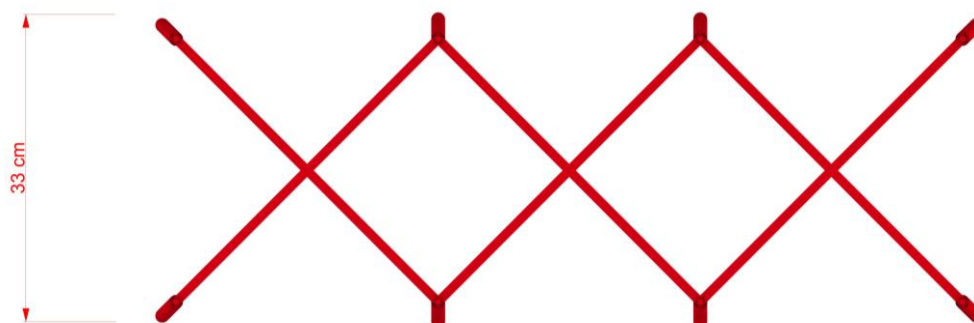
Původní varianta spojení konstrukce (archiv autorky)
